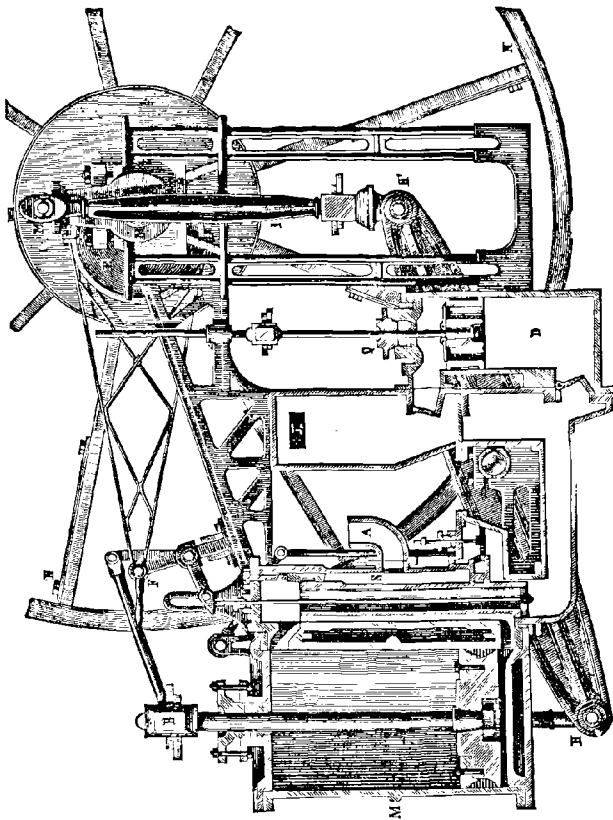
Coupe d'une machine à vapeur marine à condenseur et à balancier.
